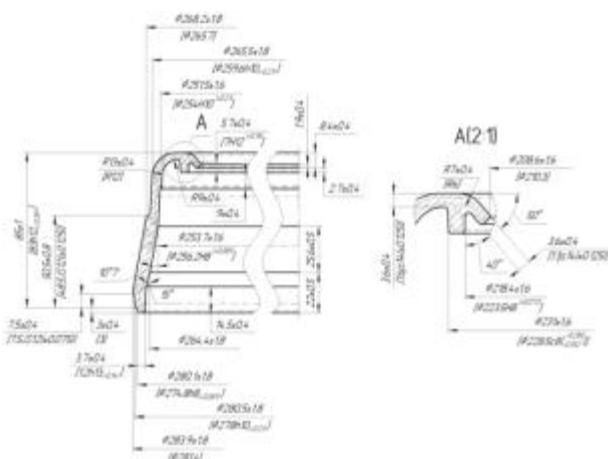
Ескіз заготовки ліття у кокіль
